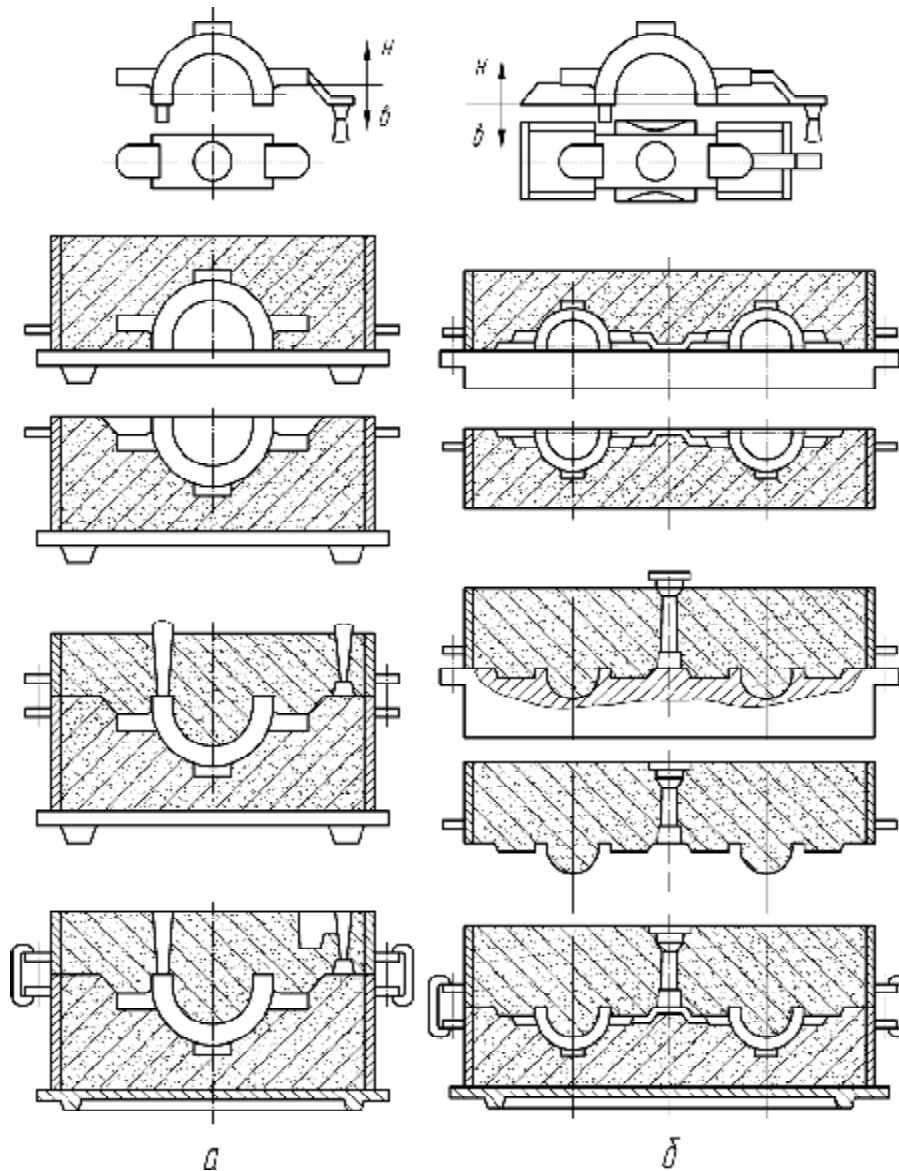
Схемы изготовления формы для получения отливки крышки подшипника вручную (а) и на машинах (б)
